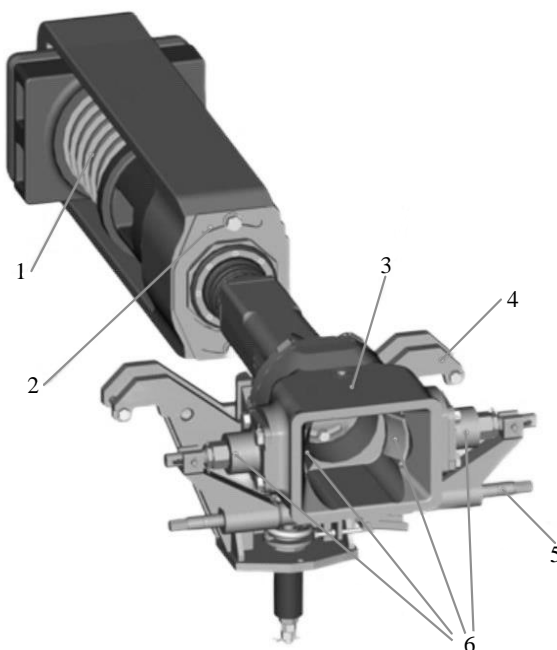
Конструкция БСУ-ТМ136 в 06 исполнении:
